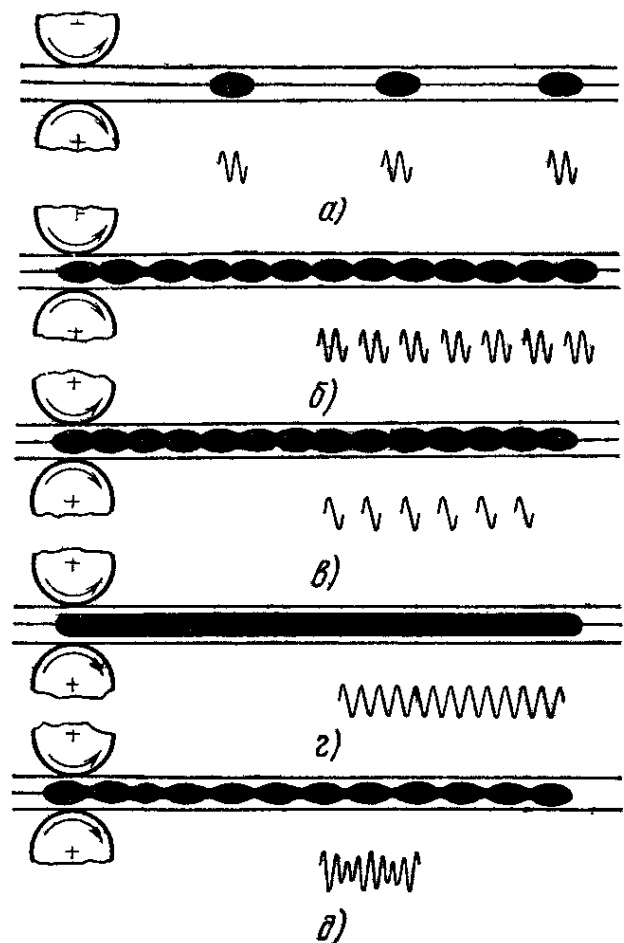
Схемы шовной сварки при разных паузах между импульсами тока
